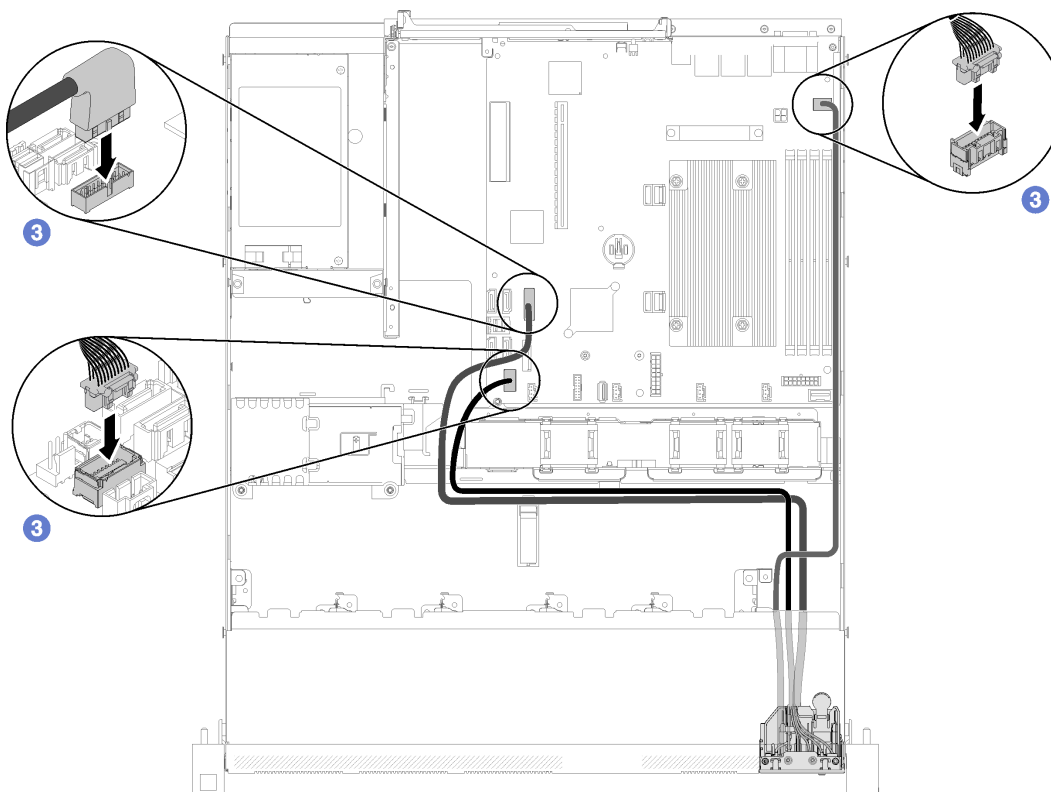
Cheminement des câbles pour le panneau opérateur avant (modèle HDD 2,5 pouces)
